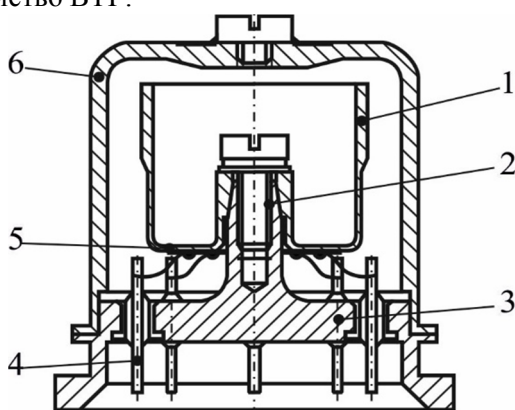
Конструкция ВТГ: 1 – резонатор; 2 – винт, 3 – основание; 4 – гермовывод; 5 – пьезоэлемент; 6 – кожух
